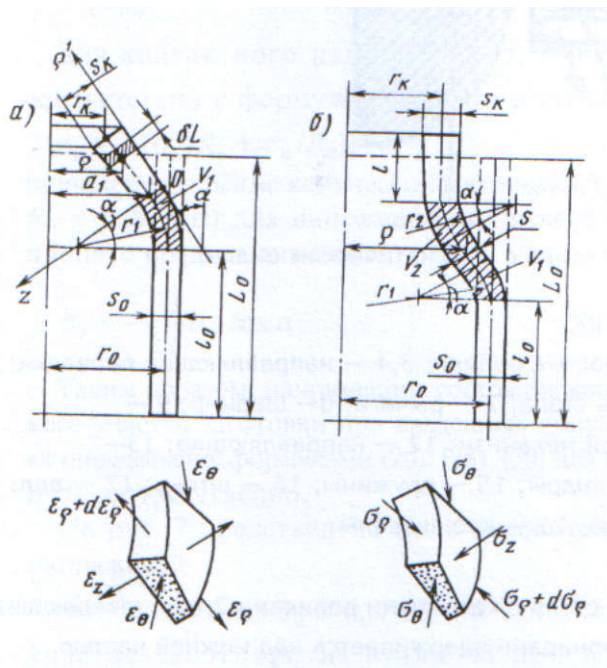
Схема обтиску трубної заготовки конічною матрицею
